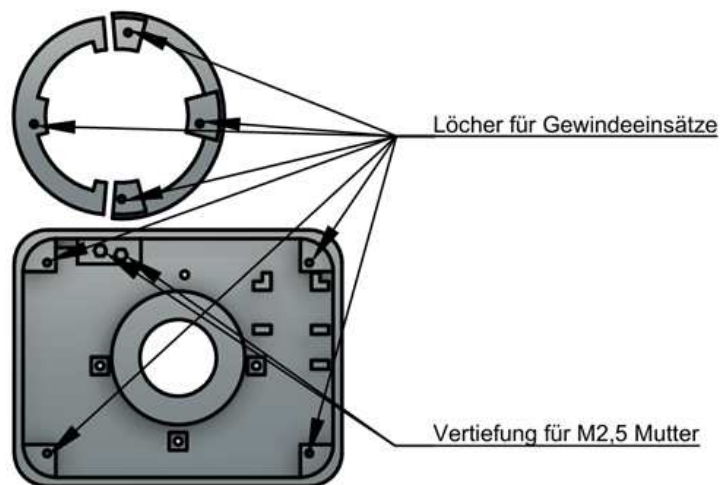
Position für Gewindeeinsätze und M2,5 Muttern
